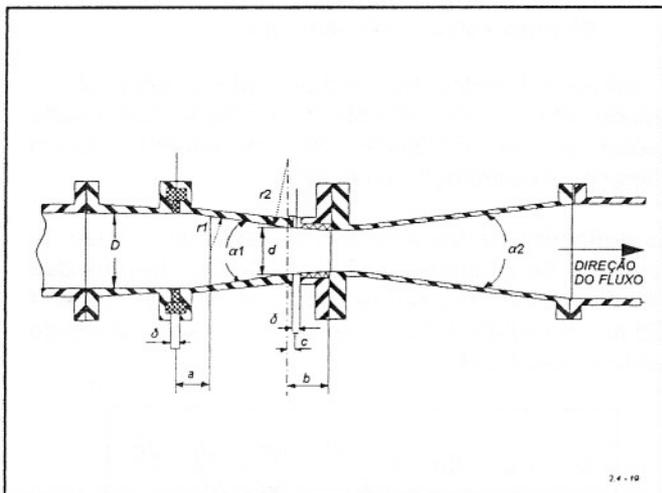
DIMENSÕES BÁSICAS DE UM TUBO DE VENTURI BÁSICO
